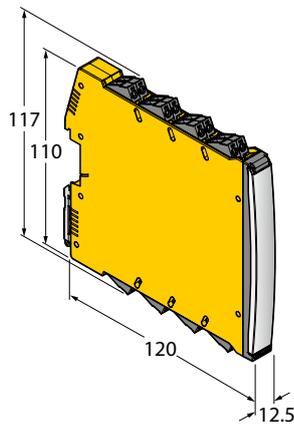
Abmessungen – Gerät mit Schraubklemmen
